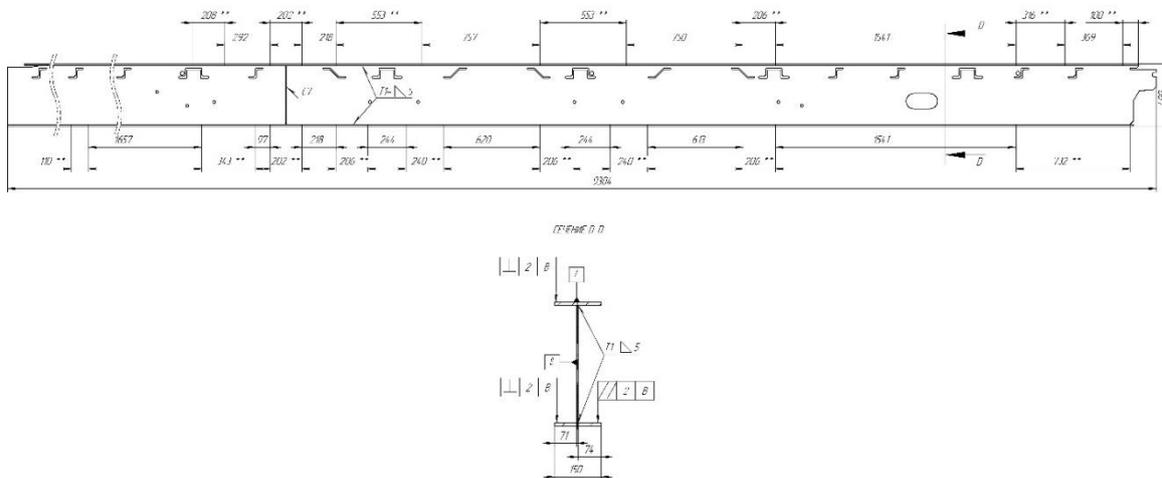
Сварочные швы лонжерона рамы шторного полуприцепа
